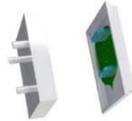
Partes diferenciadas del molde para el moldeo de una pieza.
